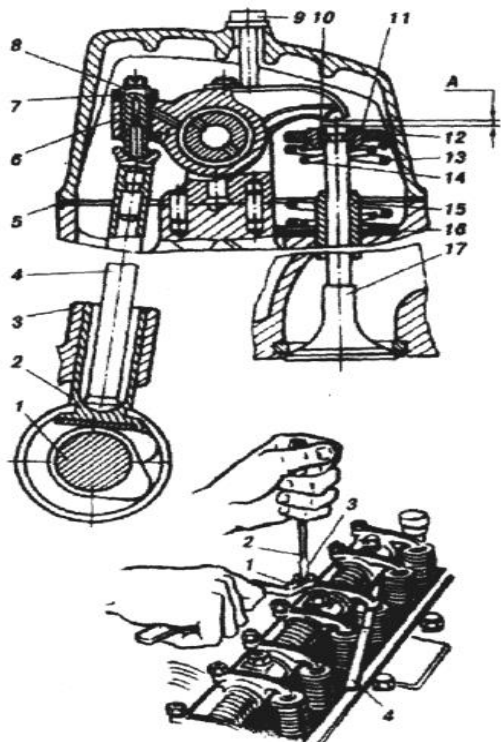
Проверка и регулировка тепловых зазоров в клапанном механизме газораспределения двигателя КамАЗ-740,10: А - тепловой зазор; 1 - распределительный вал; 2 - толкатель; 3 - направляющая толкателя; 4 - штанга; 5 - прокладка крышки; 6 - коромысло; 7 - гайка; 8 - регулировочный винт; 9 - болт крепления крышки головки; 10 сухарь; 11 - втулка тарелки; 12 тарелка пружины; 13 и 14 - клапанные пружины; 15 - направляющая клапана; 16 - упорная шайба; 17 - клапан тарелка.
